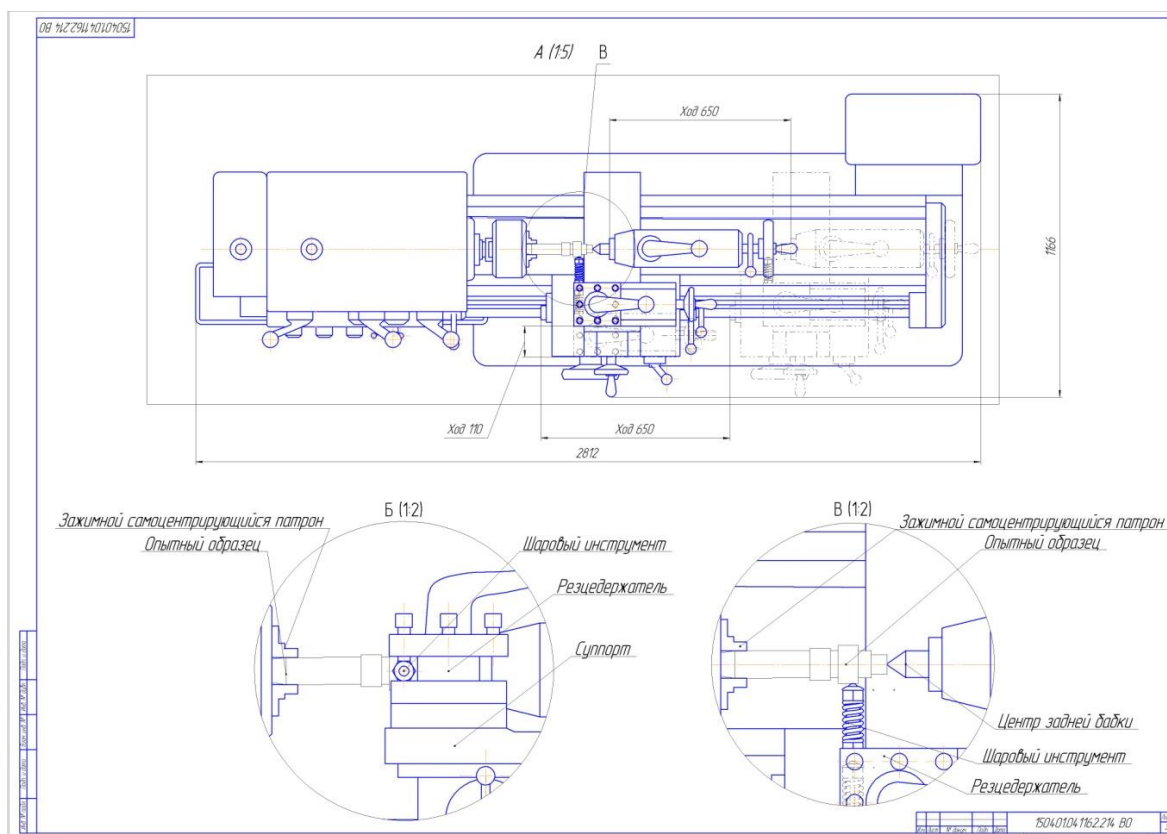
Загальний вигляд установки для деформаційної обкатки кульовим інструментом, лист 2
